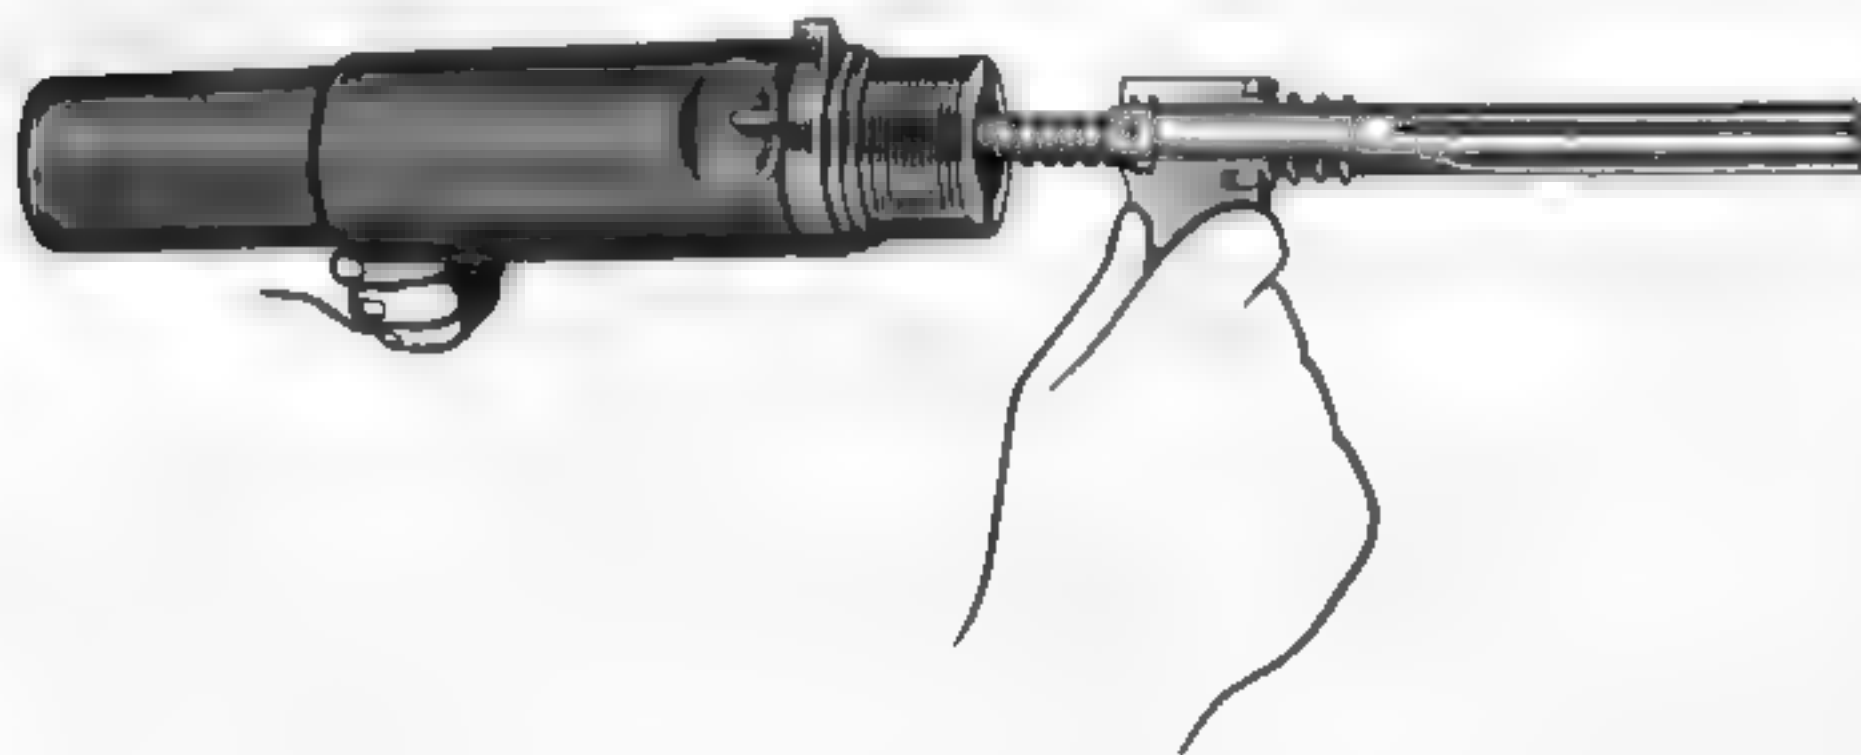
Herausnehmen des Schlosses mit Schließfeder aus dem Bodenstück
